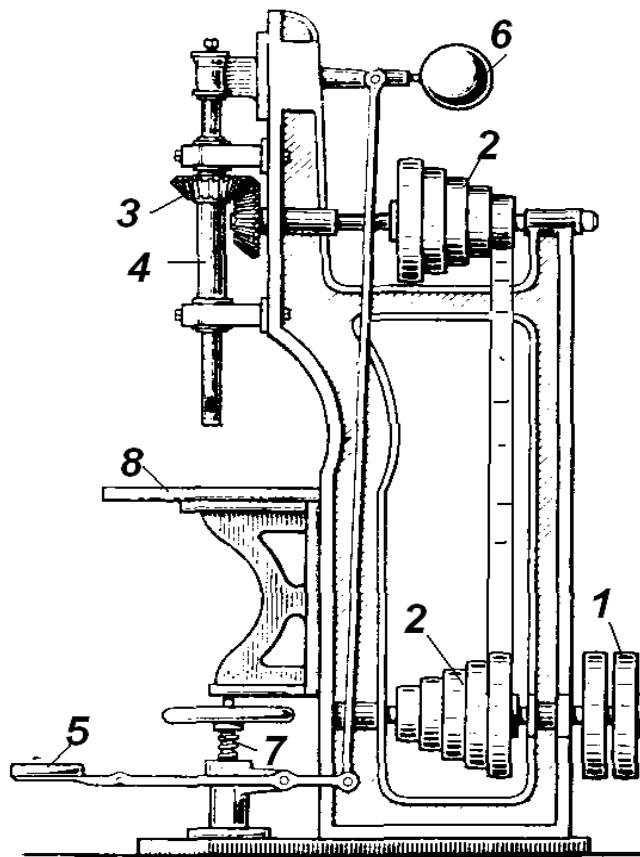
Универсальный вертикально-сверлильный станок (конструктор Дж. Несмит, 1840 г.)
